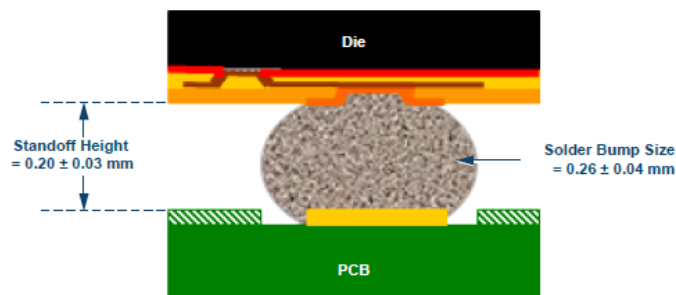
PCB装配后的AD7682/AD7689 WLCSP尺寸
